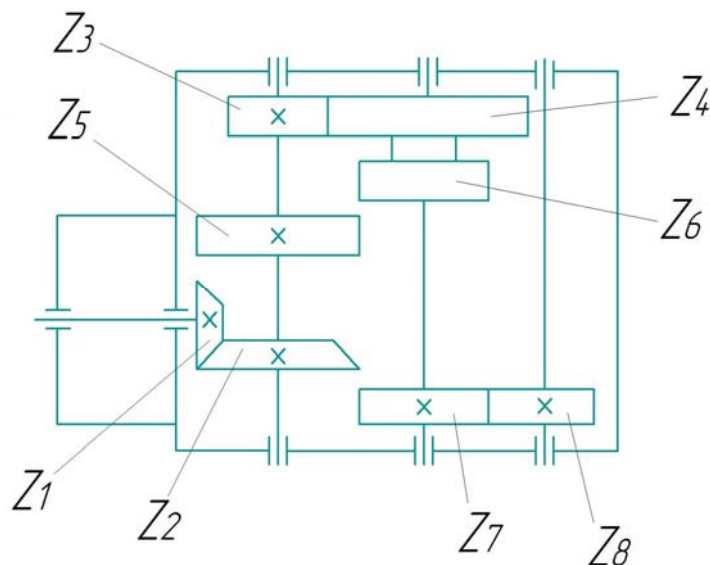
Кинематическая схема двухскоростного редуктора винтового конвейера:
